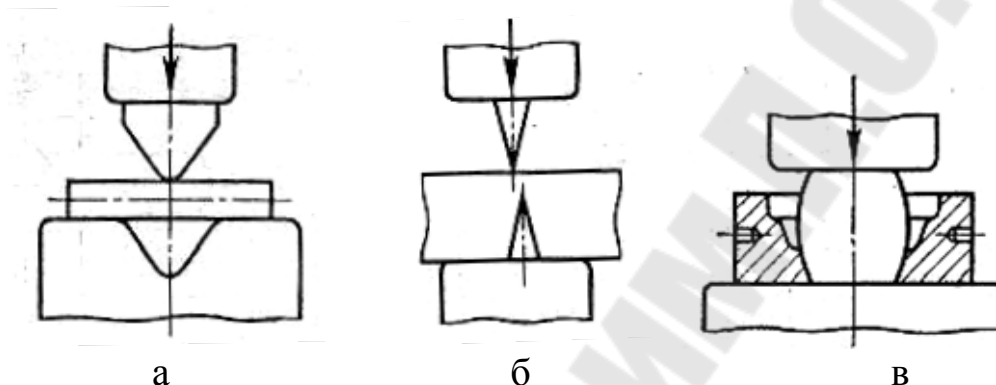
Схемы операцийковки: а – гибка; б – отрубка; в – штамповка в подкладных штампах
